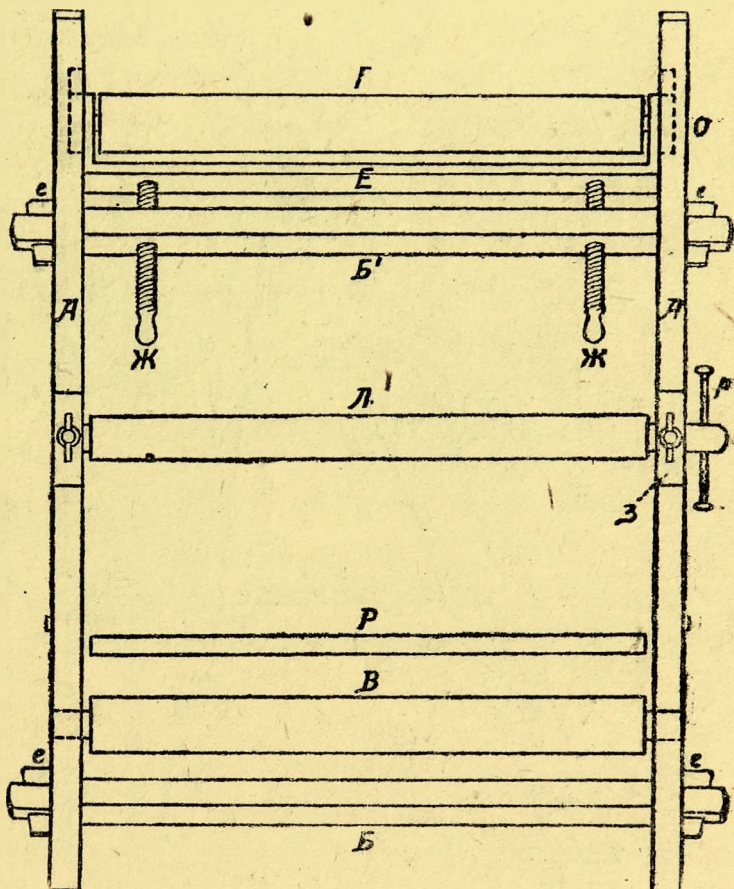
Ковровый станок для круглой основы с зевобразовательным прибором—вид спереди.
